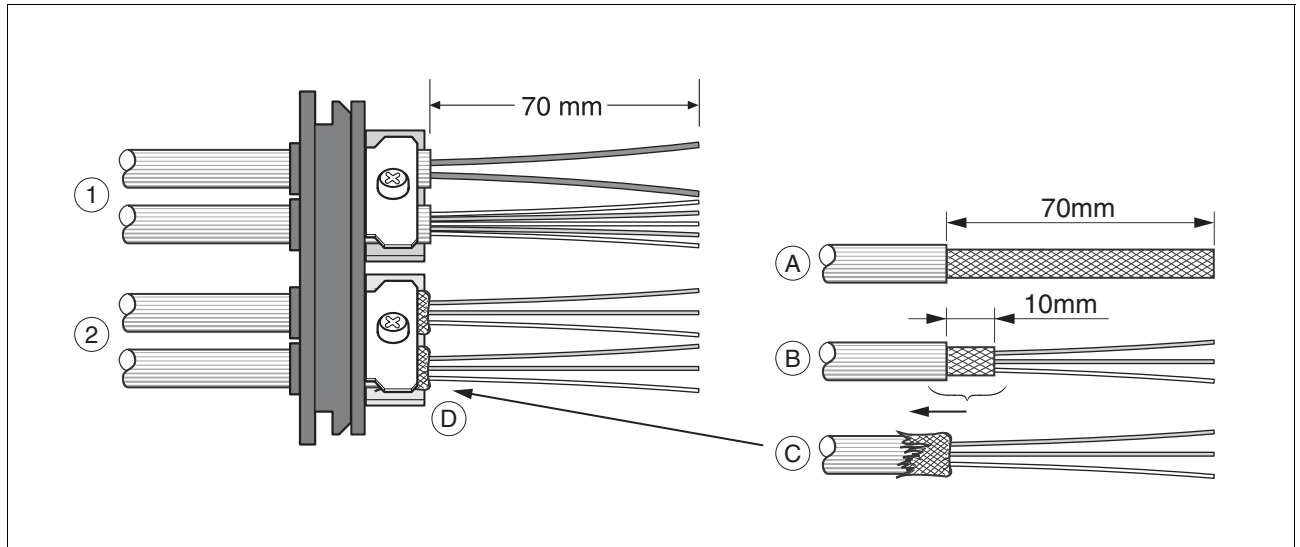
Kabel in der Kabeldurchführung befestigen
